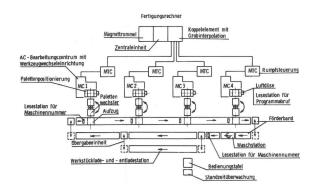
Layout eines Fertigungssystems (MAKINO MILLING)
